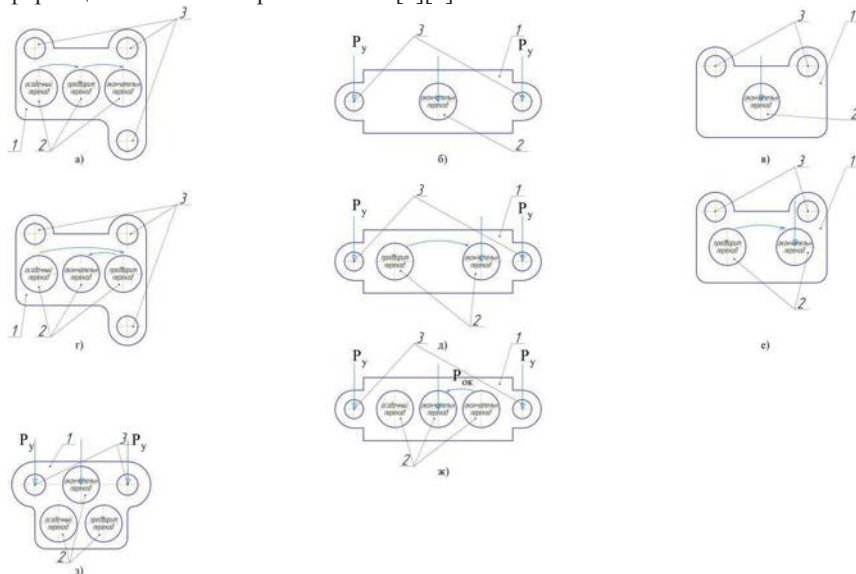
Расчетные схемы приложения нагрузок на штамповые блоки при горячей объемной штамповке: а); в); г); е) – варианты для универсальных штамповых блоков с направляющими колонками поз. 3 для одно, двух и трехпереходной штамповки с центральным в); г), эксцентричным, а); е) расположением вставки (поз. 2) для окончательного формообразования, б); д); з); ж) – варианты для специальных штамповых блоков с упругими упорами – направляющими (поз. 3) для одно, двух и трехпереходной штамповки с центральным б); з); ж), эксцентричным д) расположением вставки окончательного перехода.
